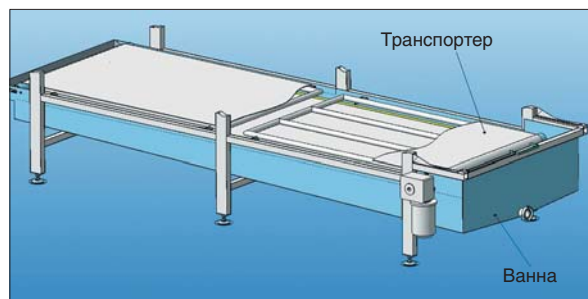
Ванна для сбора сыворотки и транспортер для выгрузки готового продукта
